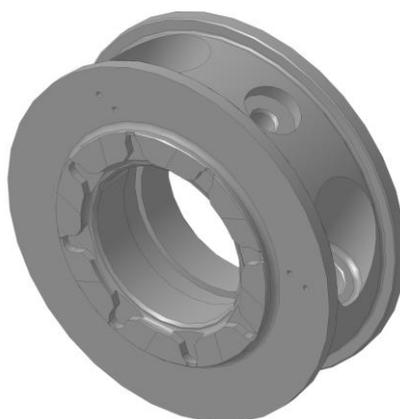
3D-модель подшипника опорно-упорного
